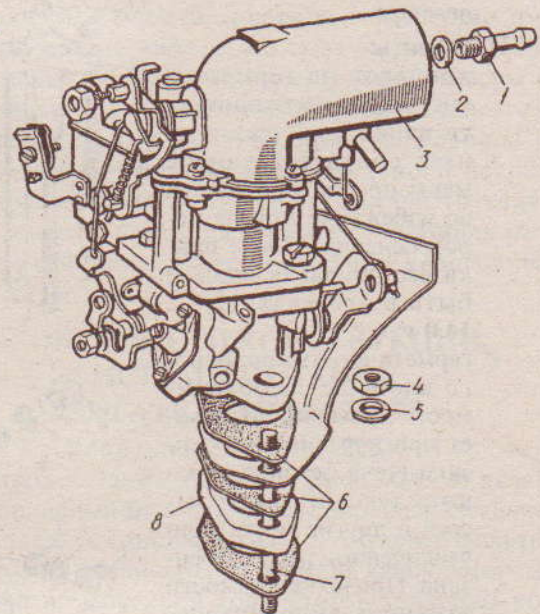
Карбюратор К-133А (с 10.82 г.): 1 - штуцер топливоподводящий; 2 - прокладка; 3 - карбюратор К-133А; 4 - гайка М8; 5 - шайба 8 стопорная; 6 - прокладка фланца карбюратора; 7 - шпилька крепления карбюратора; 8 - проставка карбюратора
